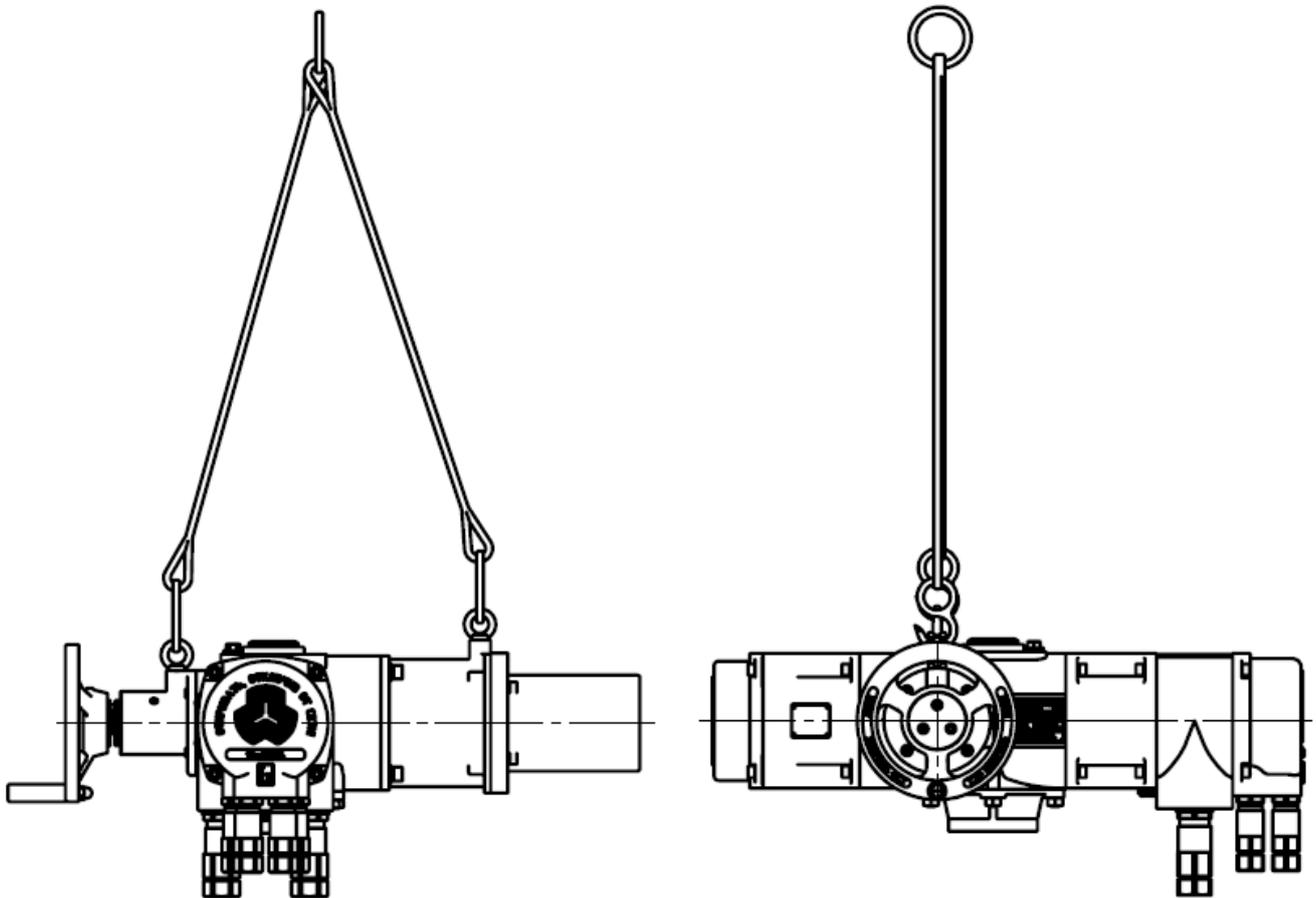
б – Схема строповки привода конструктивной схемы 41
